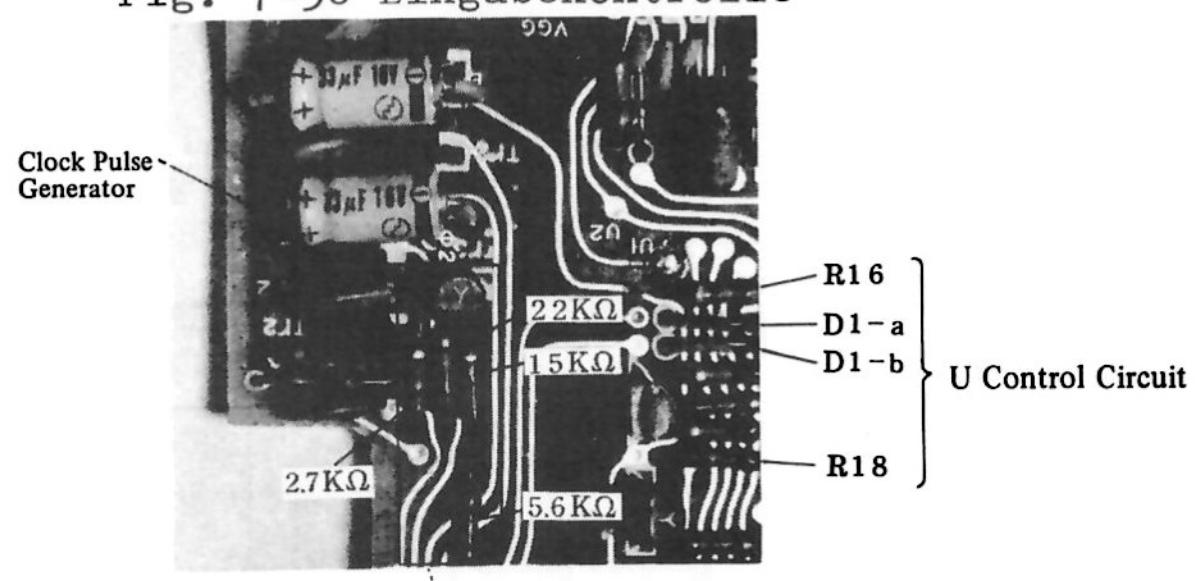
Lageplan der Eingabekontrollschatzung
